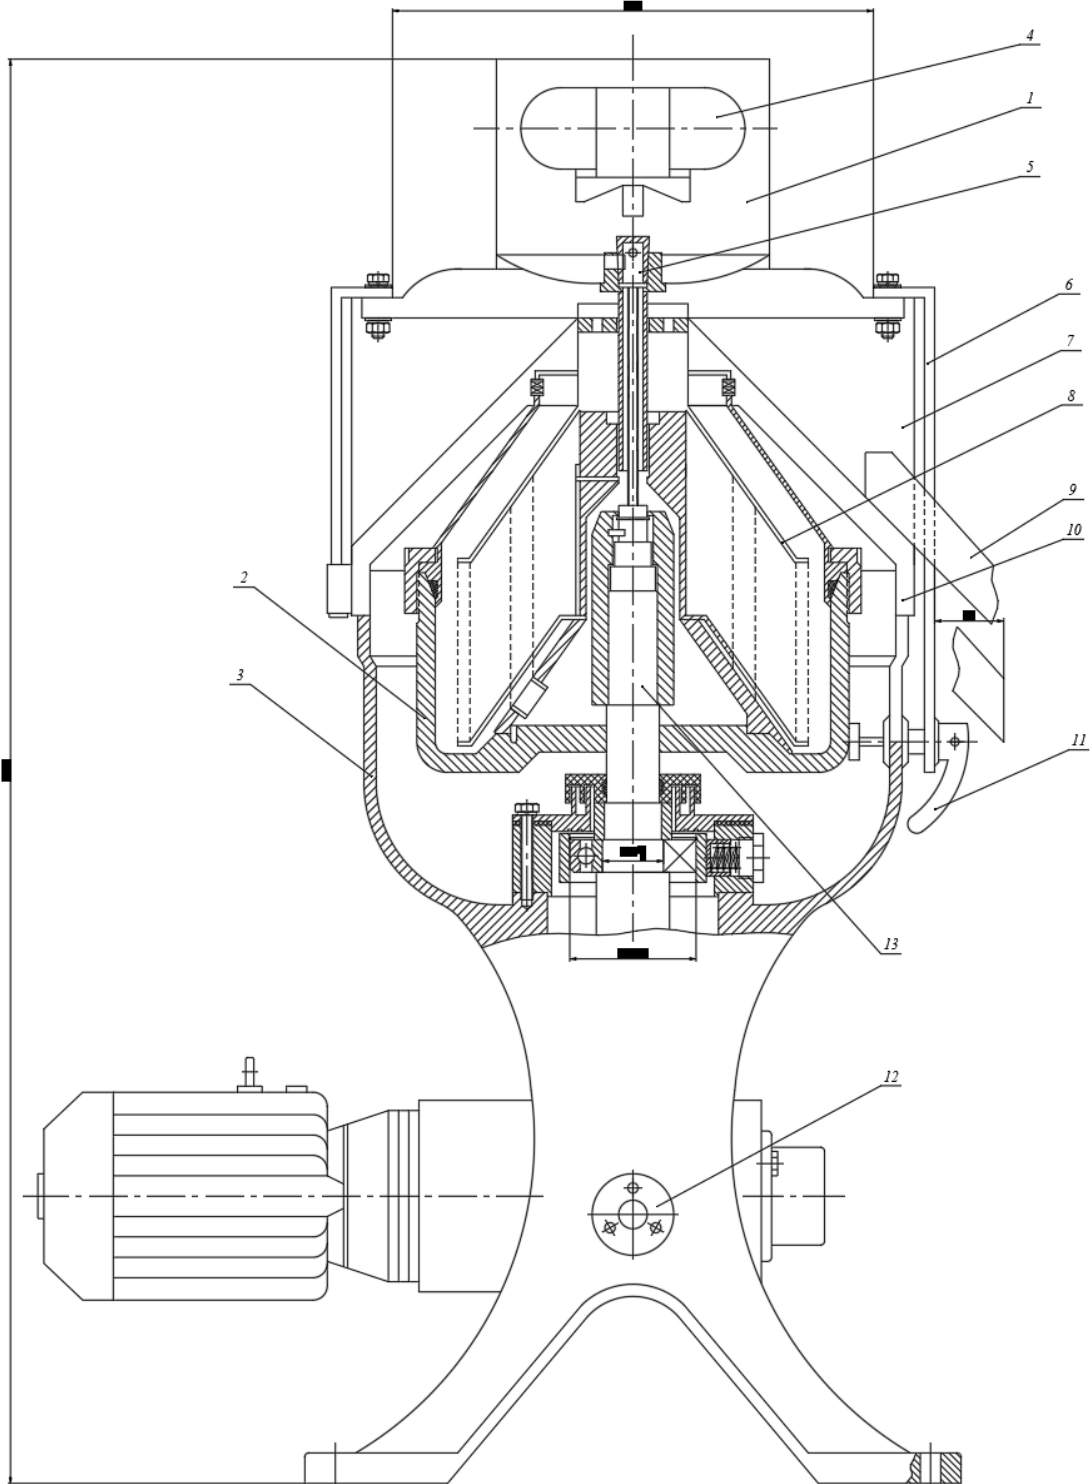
Загальний вигляд сепаратора-вершкоутворювача
